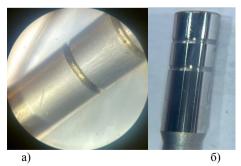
Торцевая поверхность штока управляющего клапана (мультипликатора) со следами изнашивания (а), торцевая поверхность нового штока управляющего клапана (б)
